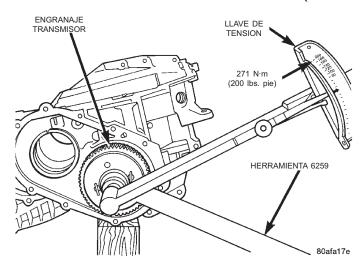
Apriete el engranaje transmisor con una torsión de 271 N·m (200 lbs. pie)
